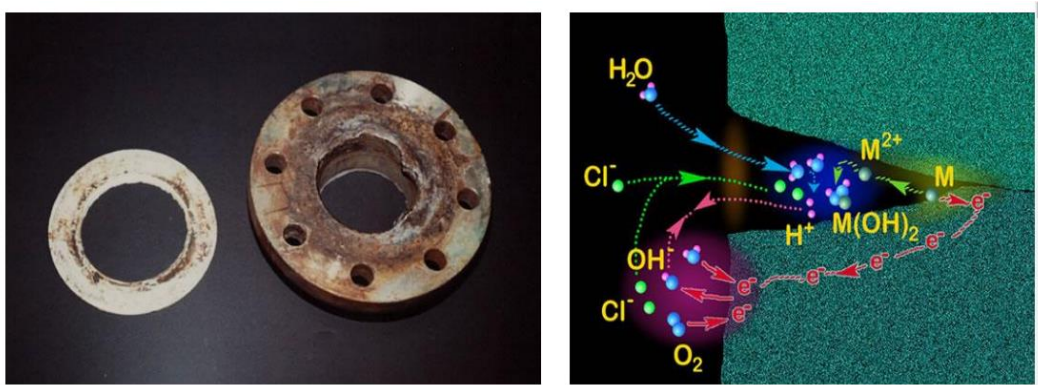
Aspect et mécanisme d'attaque de la corrosion caverneuse.
